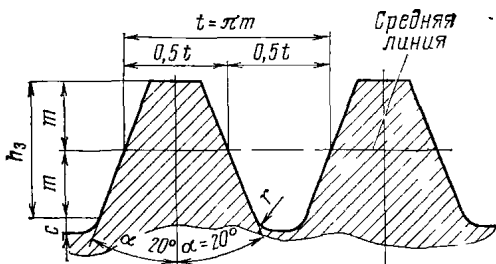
Исходный контур цилиндрических зубчатых колес эвольвентного зацепления
